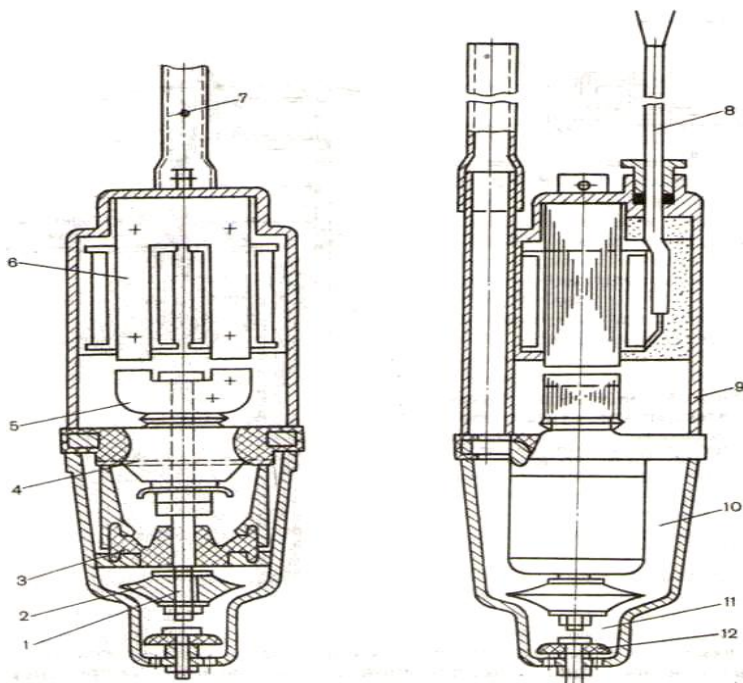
Вибрационный насос: 1 – шток; 2 – рабочий орган; 3 – диафрагма; 4 – резинометаллический элемент; 5 – якорь; 6 – электромагнит; 7 – напорный патрубок; 8 – кабель; 9 – корпус; 10, 11 – нагревательная и всасывающая камеры; 12 – обратный клапан
